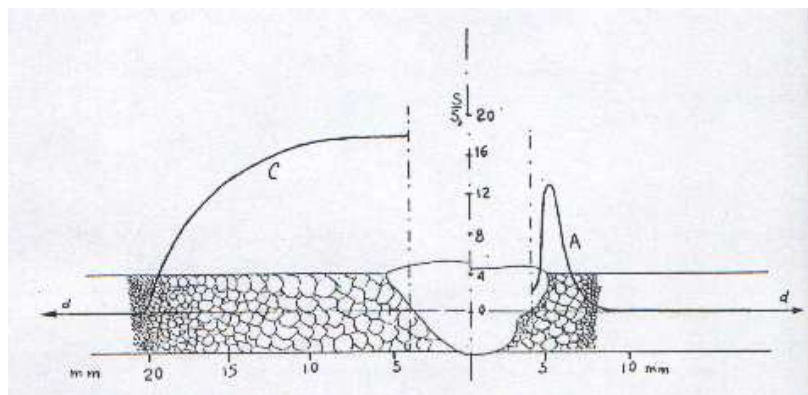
Influencia del ciclo térmico de soldadura sobre las dimensiones del grano del metal base
